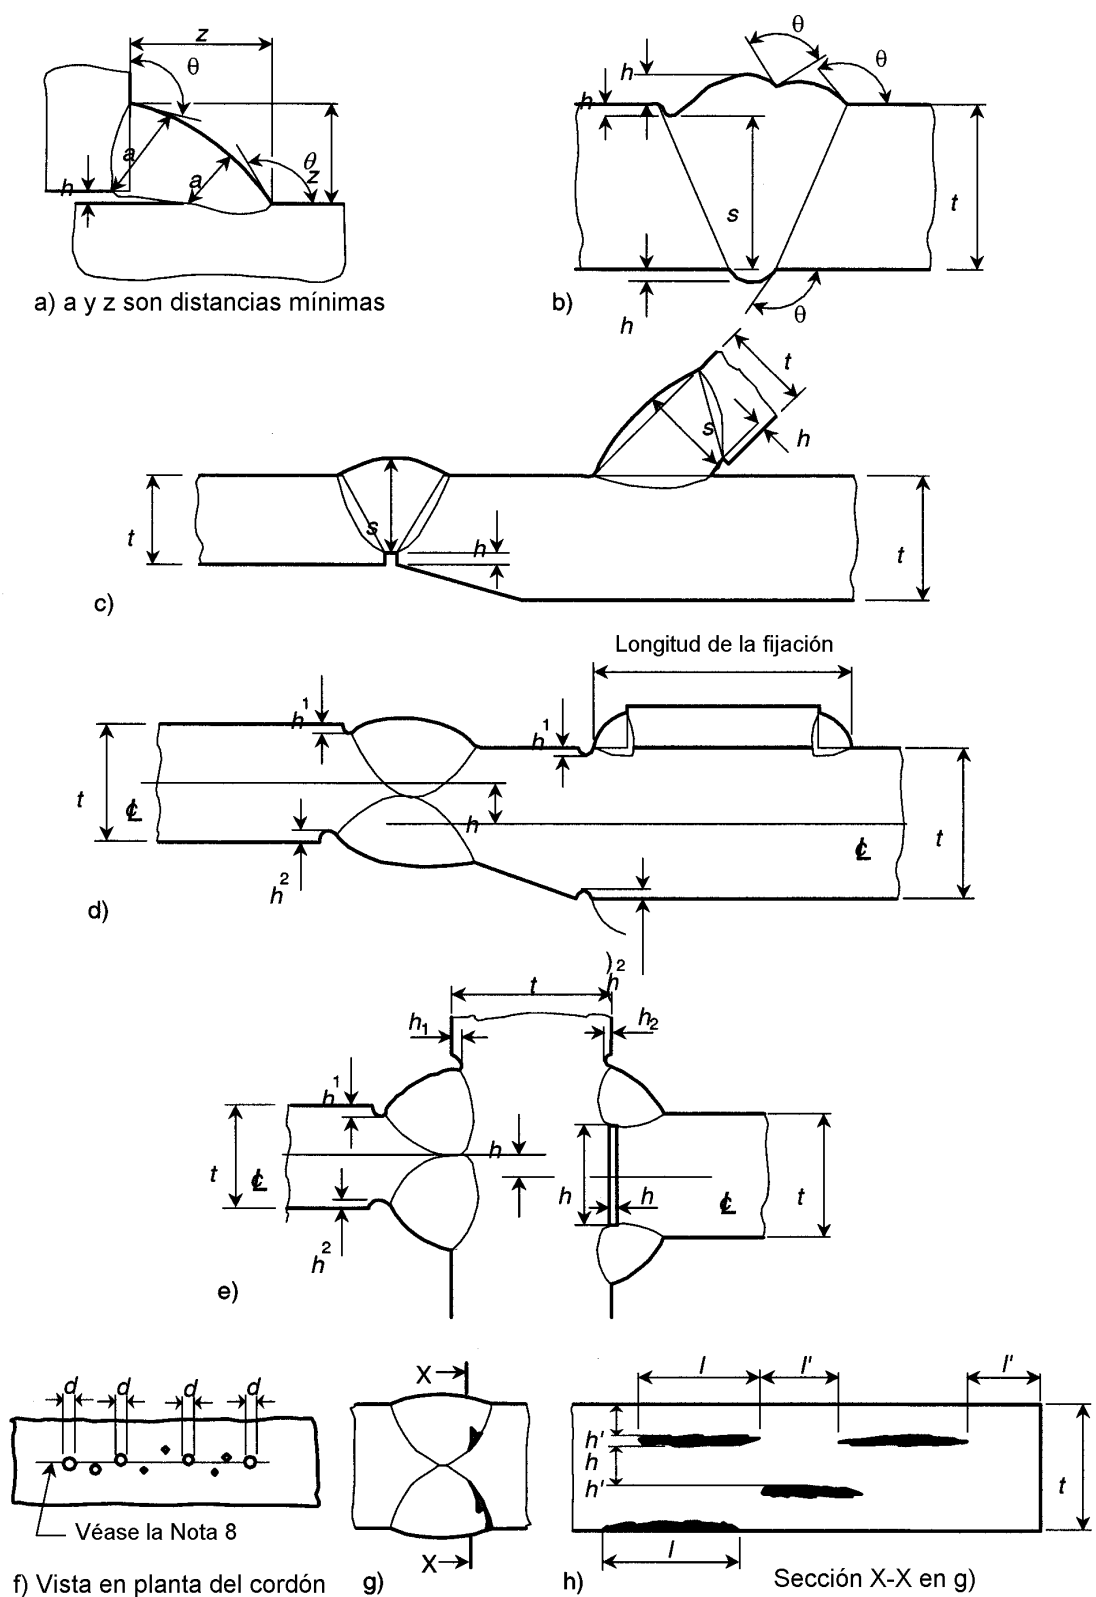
Dimensiones de las discontinuidades de soldadura
